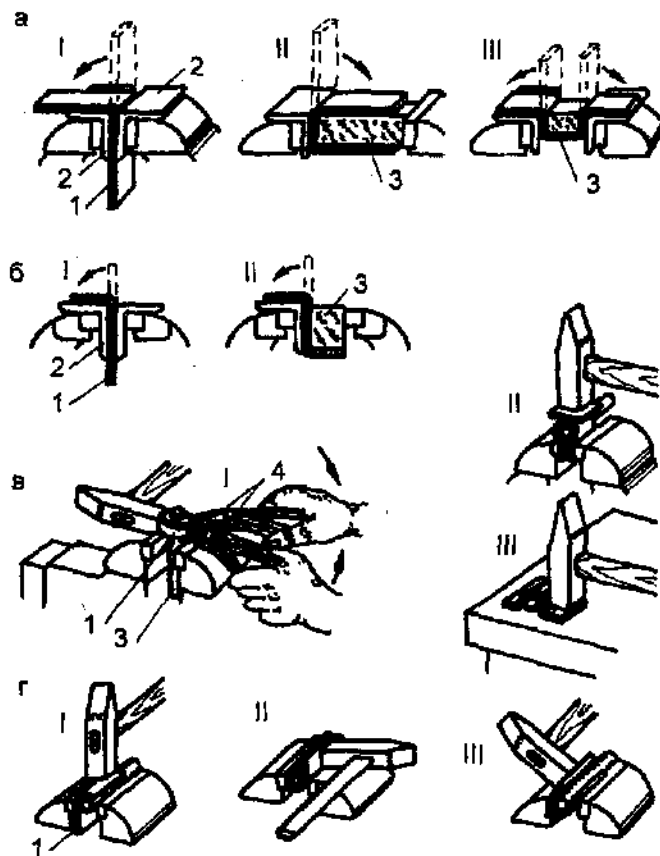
Гибка прямоугольной скобы (а), двойного угольника (б), хомутка (в) и втулки (г): 1 — заготовка; 2 — уголки-нагубники; 3 — оправка; 4 — плоскогубцы
